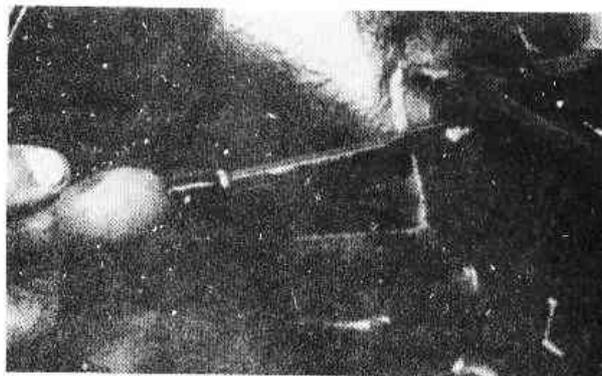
Снятие заглушки стопорного штифта — коробка передач типа В (Разд.3)
